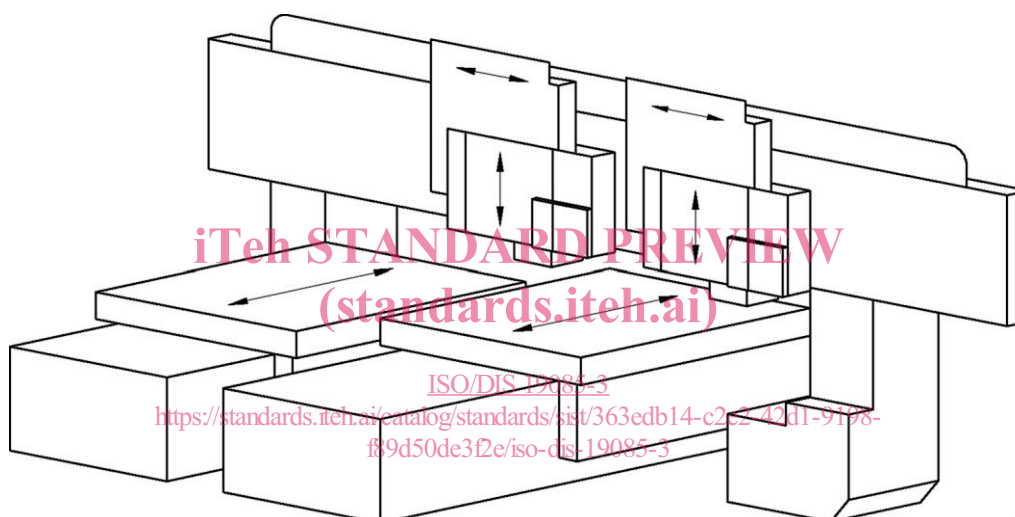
Exemple de machine à portique avec tables mobiles, portique fixe, têtes d'usinage mobiles
